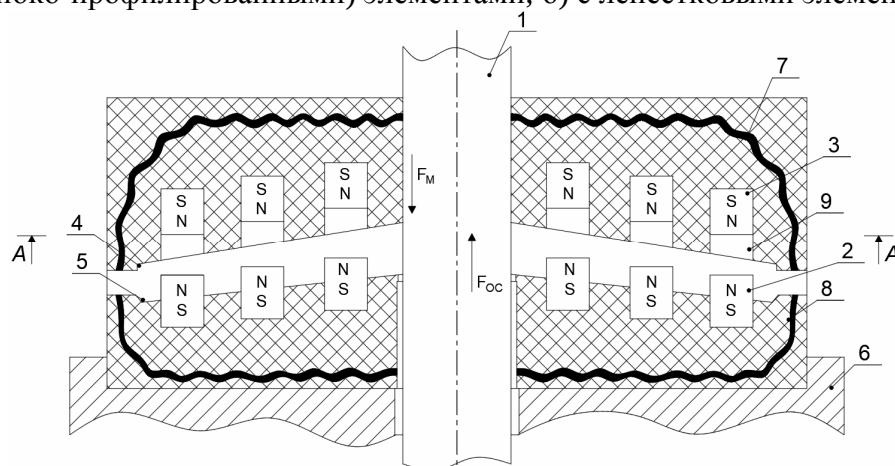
Адаптивный демпфер с волновыми элементами жесткости: 1 – вал; 2, 3 – постоянные магниты; 4, 5 – конусы; 6 – корпус; 7, 8 – стаканы; 9 – канавка
